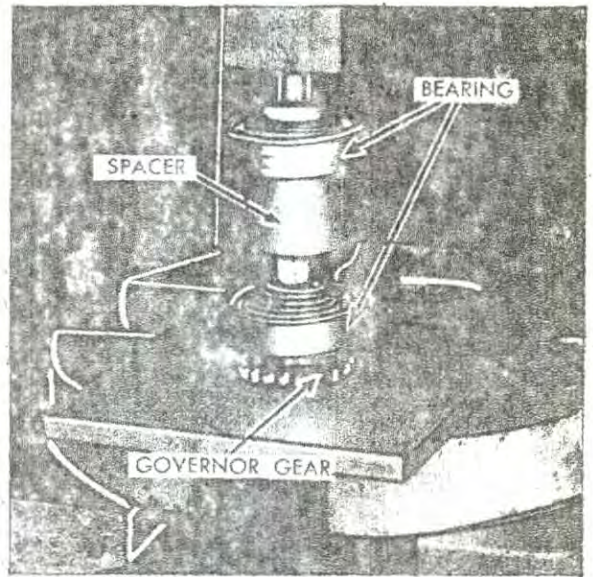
Conjunto de impulsión del regulador tipo hidráulico.
